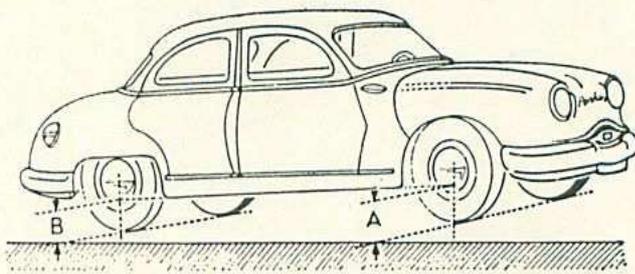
Hauteurs de caisse en fonction de la dimension des pneus
